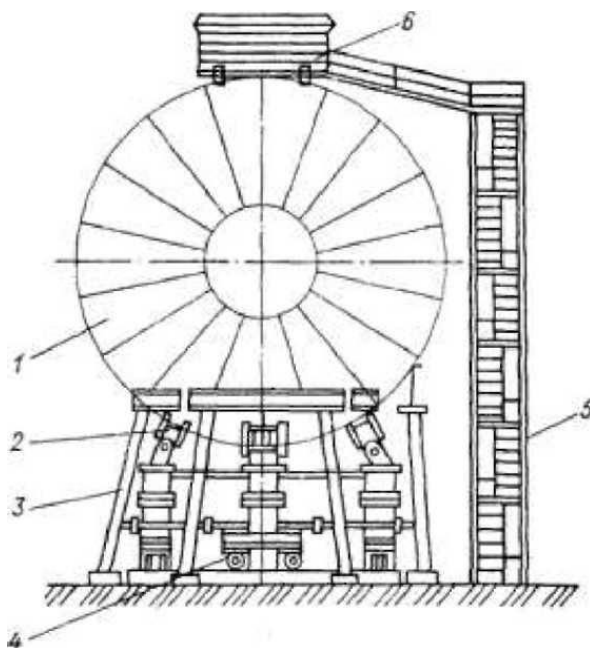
Схема установки шарового резервуара при сварке на манипуляторе Г.С. Сабирова
